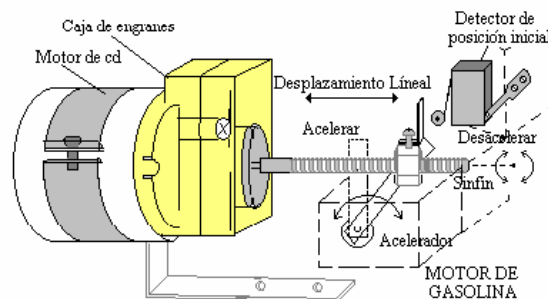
Acoplamiento mecánico del motor al sinfín, y el detector de posición inicial
